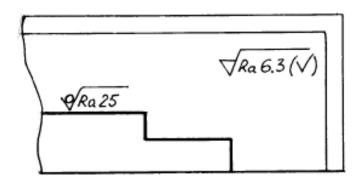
Пример обозначения шероховатости, одинаковой для части поверхностей
